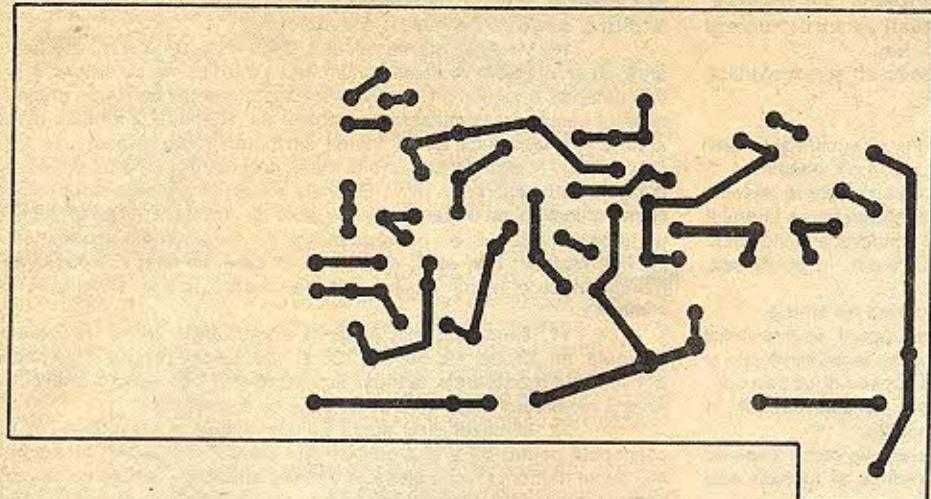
DESENUL CIRCUITULUI IMPRIMAT PENTRU OSCILATORUL DE RADIOFRECVENTA, SEPARATOR SI MODULATOR SC. 1:1
